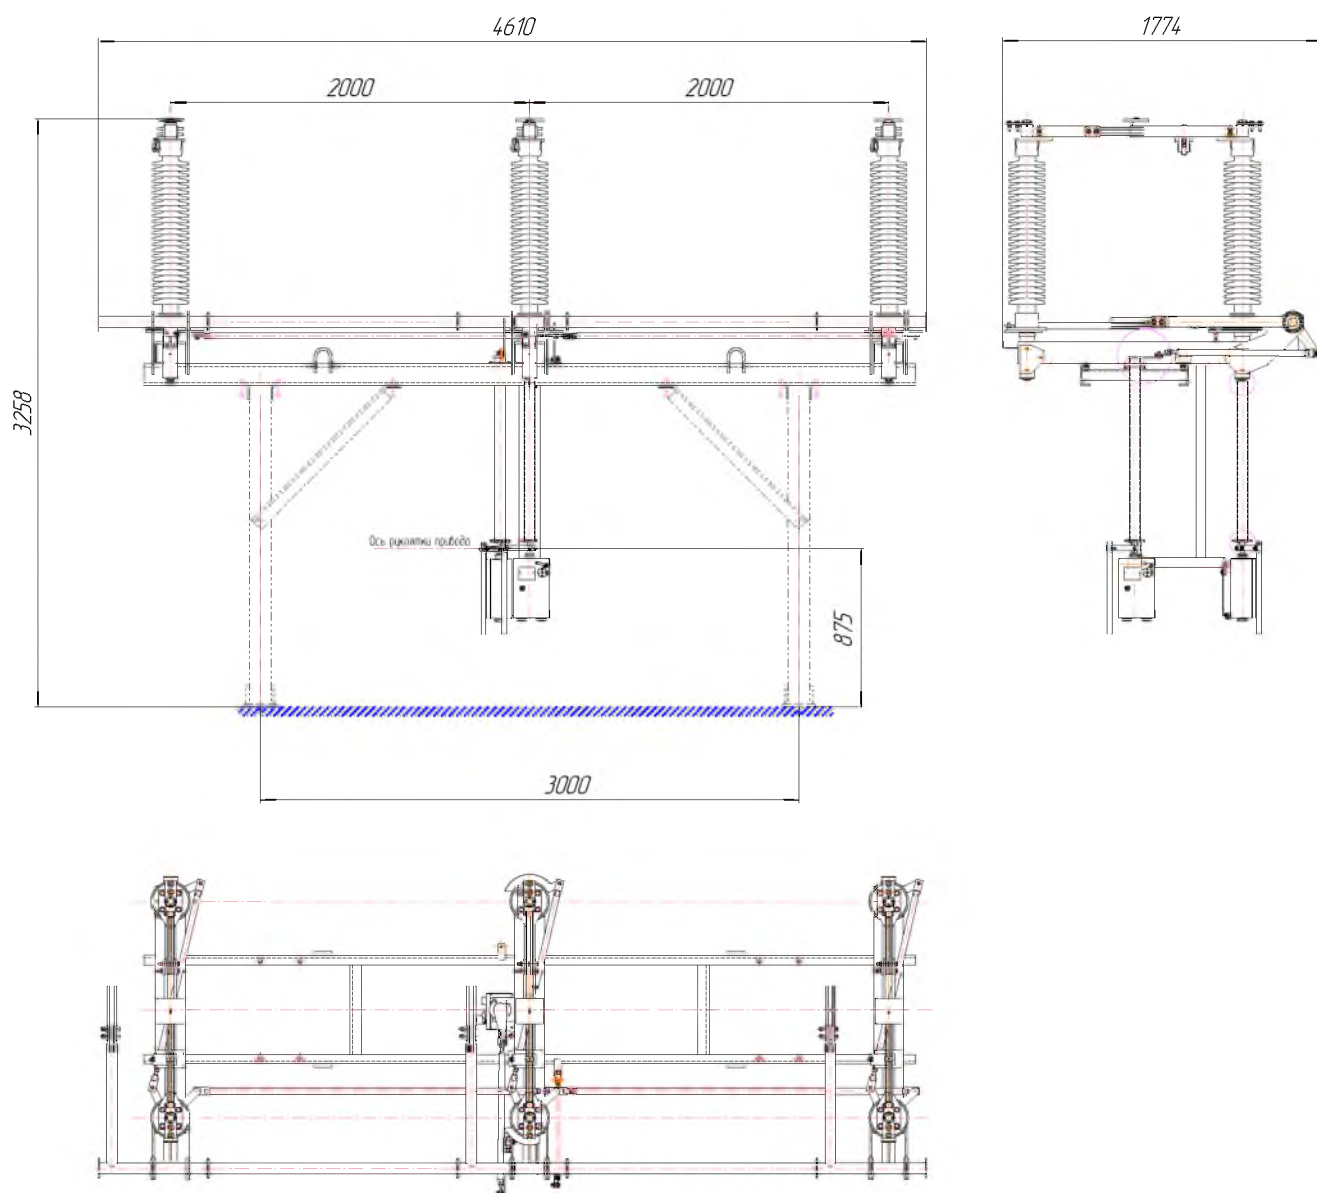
Общий вид разъединителя РГП СЭЦ®-110
